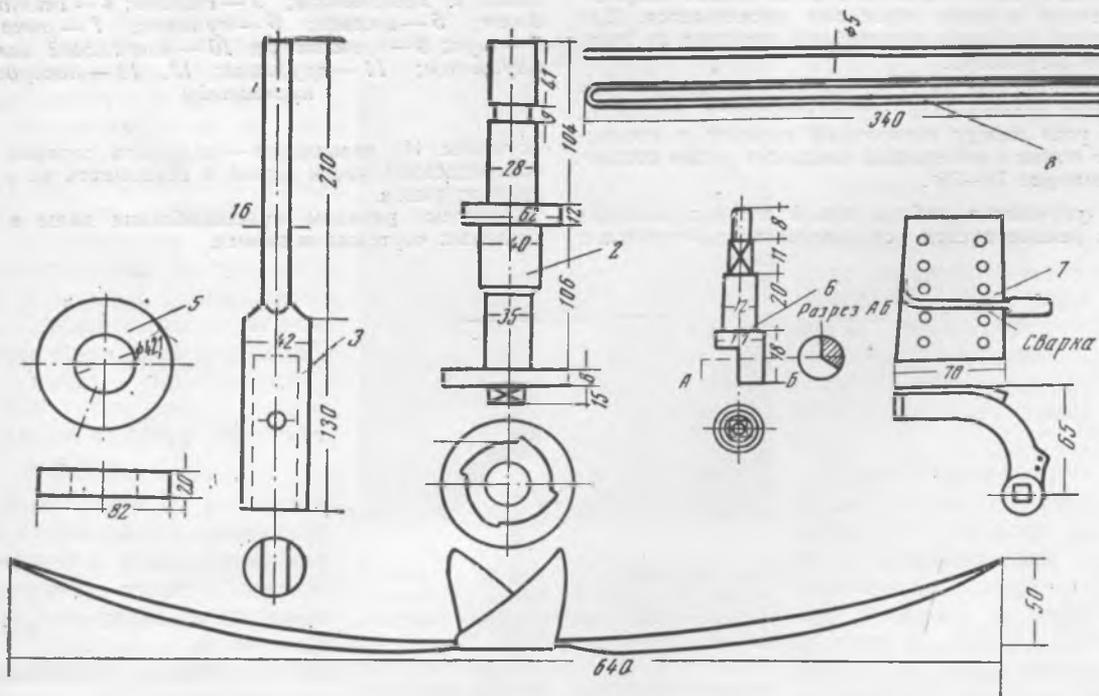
Рабочий орган для обработки почвы в рядах посадок (правый), внизу — нож крестообразный; 2 — валик поворотный; 3 — стойка; 5 — кольцо; 6 — кулачок; 7 — рычажок; 8 — шуп.
